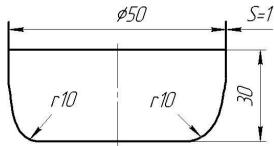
Деталь изготовления вытяжкой с прижимом
